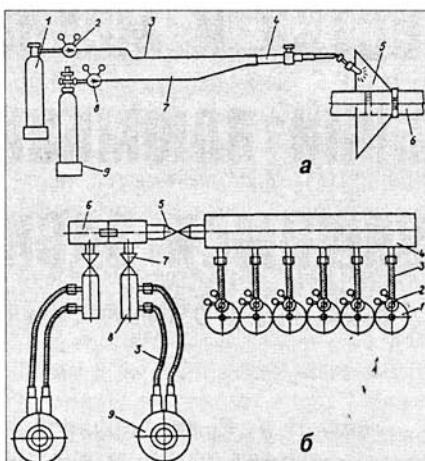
Схемы постов для термообработки сварных соединений трубопроводов с использованием газопламенного нагрева:
